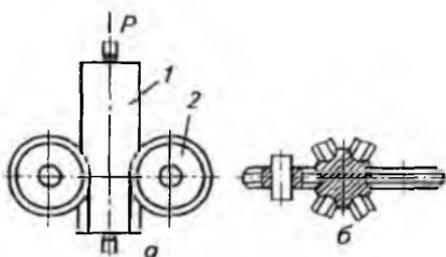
Схема раздачи (а) и калибрования (б) шлицев:
